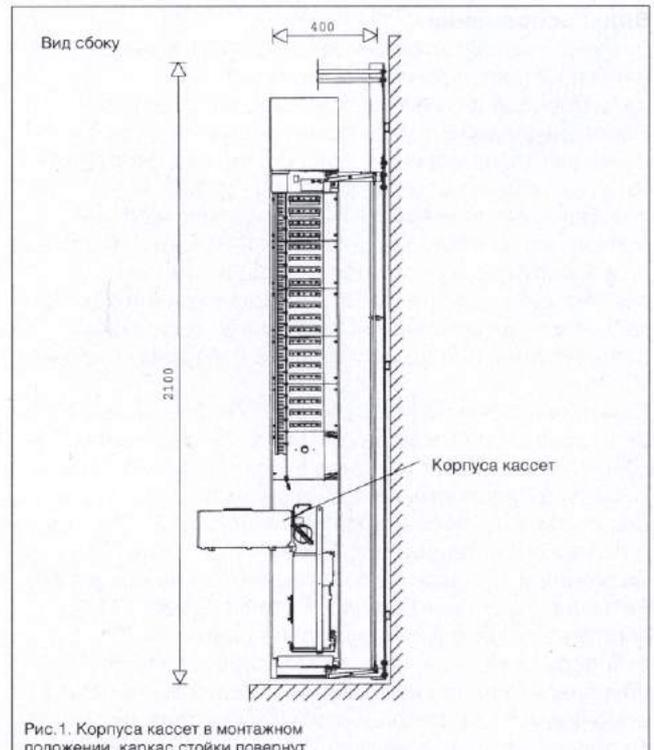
Корпуса кассет в монтажном положении, каркас стойки повернут
